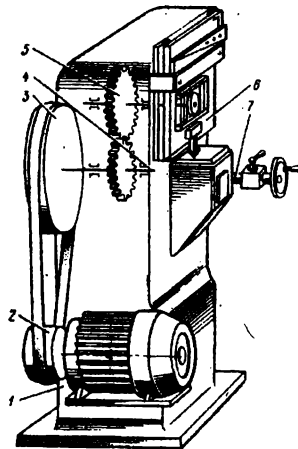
Станок ПШП-2 для обрезки и насечки зубьев
